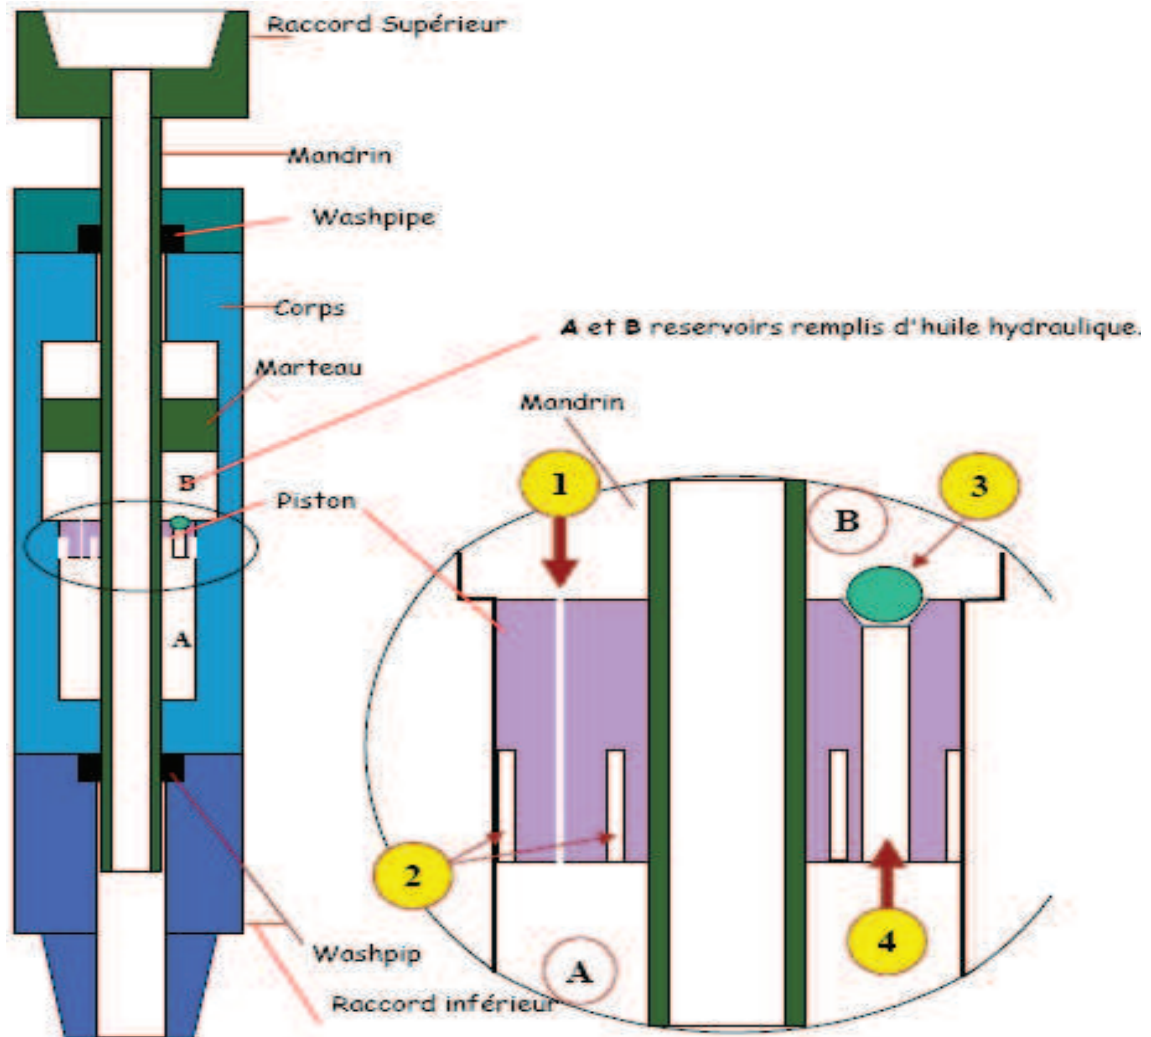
Schema d'une coulisse hydraulique. [8]
